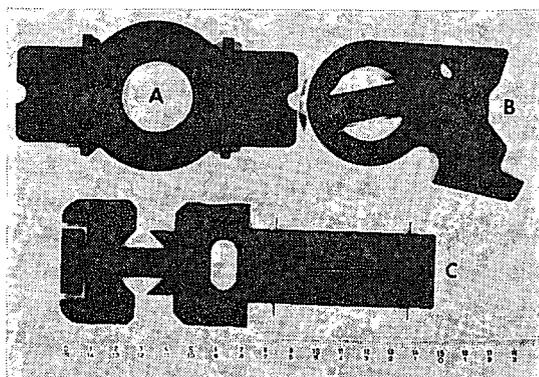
Exemplos de peças recortadas com uma máquina-ferramenta comercial usando um laser de CO_2 de 600 W. A — aço de construção, espessura 3 mm; B — idem, 5 mm; C — alumínio, 2 mm.
